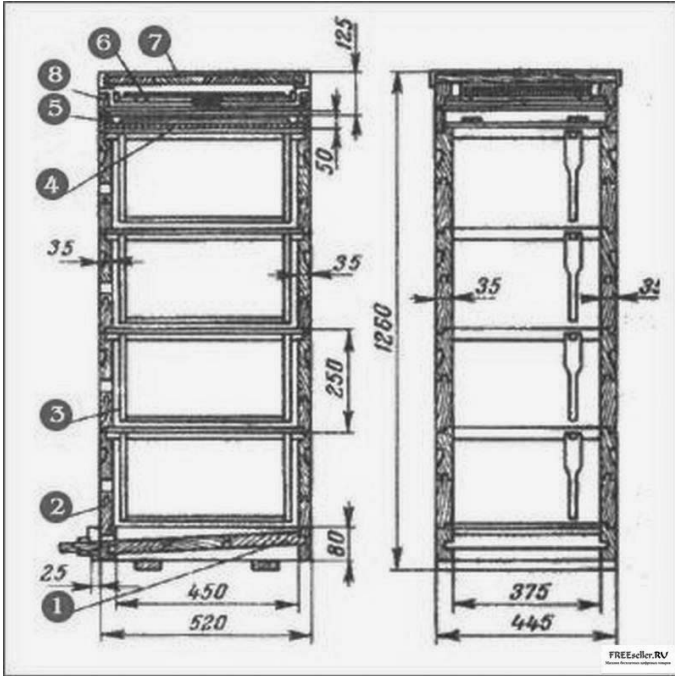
Схема. 1 – дно; 2 – корпус; 3 – рамка; 4 – потолок; 5 – подкрышник; 6 – вентиляционная рама; 7 – крыша.
